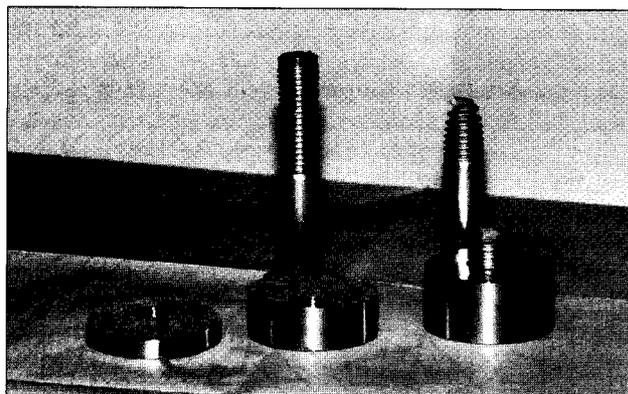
Kugelformig geplatzte Mutter PAN-16/5.6. Links: Versuch 21; rechts: Versuch 22
